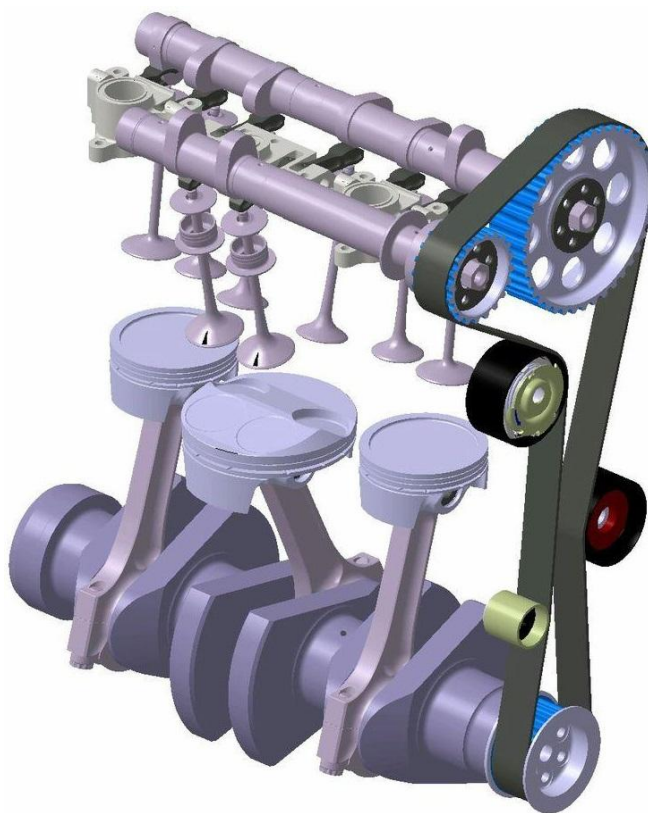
Časování ventilů u motoru 1NZ-FXE - Toyota Prius [3]
